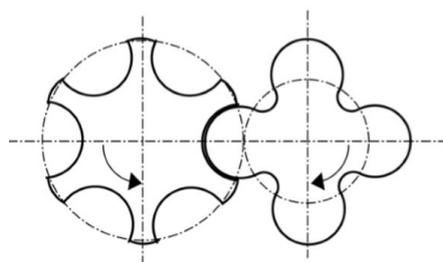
Corte transversal dos rotores de um compressor de parafusos [2]
